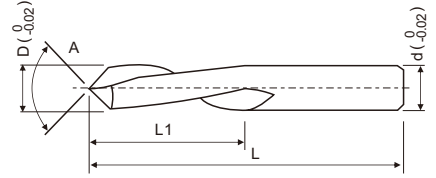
铝用不涂层 AL Uncoated	Fig.2	黑色涂层 Black Coating	Fig.3	古铜色涂层 Bronze Colored Coating	钻尖角度 A Drill point angle	刃径 D Outside Diameter	柄径 d Shank Diameter	刃长 L1 Flute Length	总长 L Total Length	Order Number
